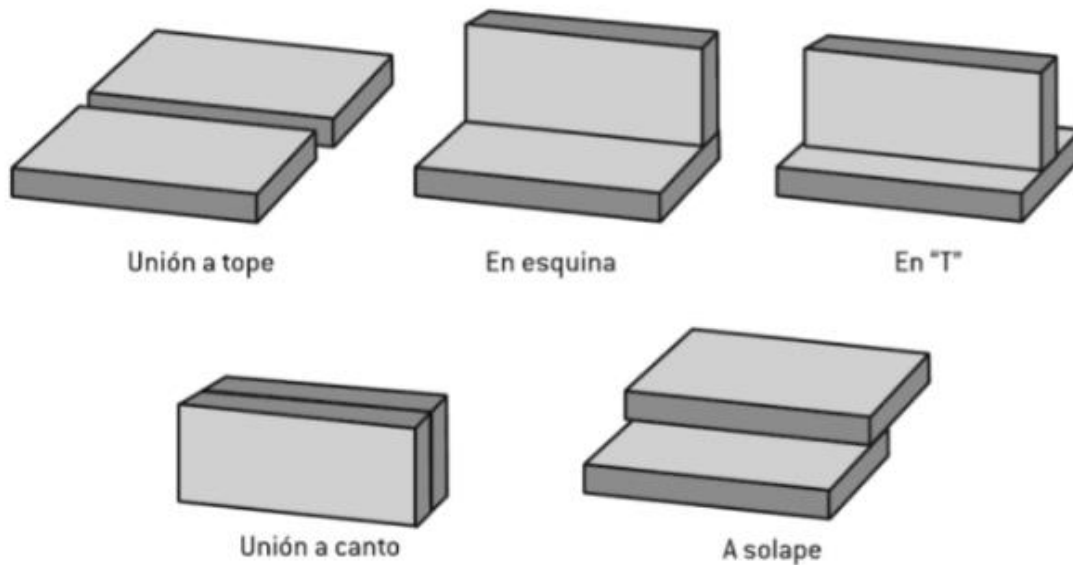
Tipos de uniones. Interpretación de soldadura UF1640
